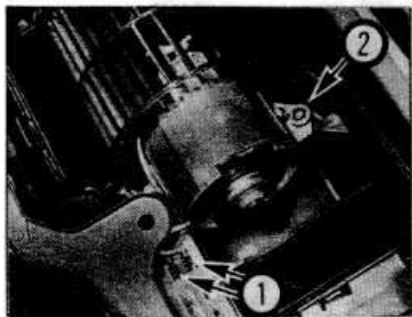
Отсоединение вакуумной трубки от корпуса электродвигателя вентилятора
